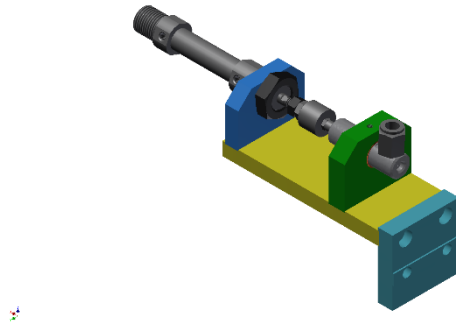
Subconjunto do sopro colocado na parte móvel da máquina
